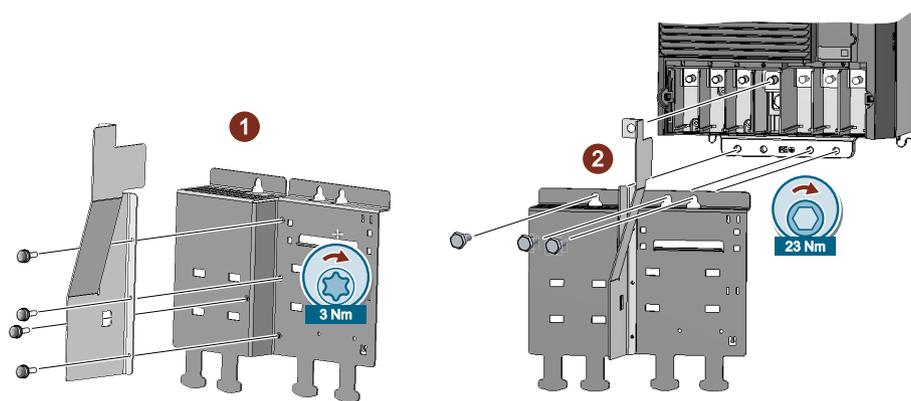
Montaje de la chapa de pantalla inferior, FSF
